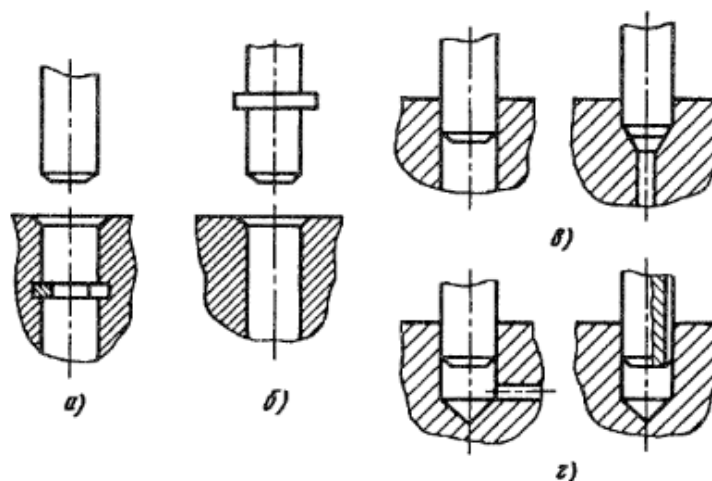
Соединения с элементами фиксации относительного положения деталей в процессе их сборки (*а, б*) и наличием выхода воздуха при запрессовке деталей в отверстие (*в, г*)
